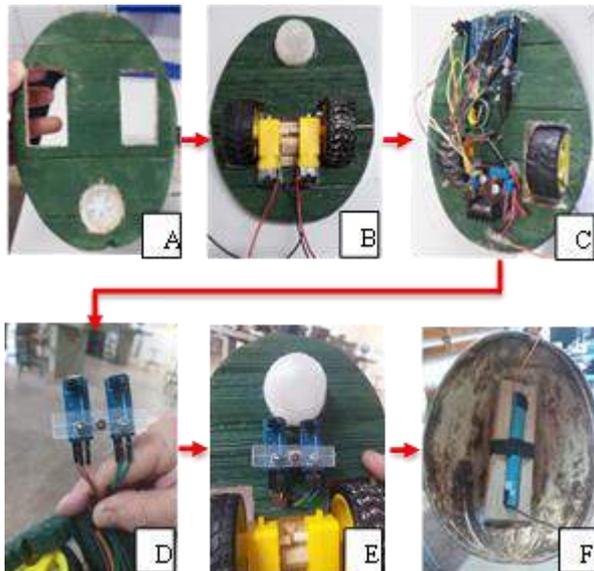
Montagem do protótipo, (A) Preparação do chassi para receber o rodízio giratório e rodas, (B) Fixação do rodízio giratório e sistemas de motores e rodas, (C) Montagem do Arduino e a ponte H no chassi do robô, (D) Montagem e instalação dos sensores de linha, (E) Fixação dos seguidores de linha no chassi e (F) Baterias
